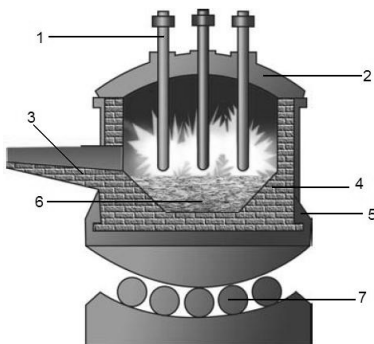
Схема електродугової печі: 1– електрод; 2 – склепіння; 3 – жолоб для випуску готового металу; 4 – вогнетривка футеровка; 5 – кожух; 6 – шихта; 7 – механізм нахилу печі
